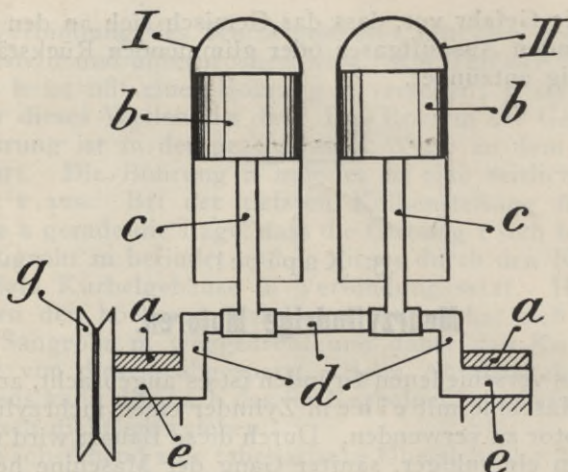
Schema eines Zweizylindermotors mit parallel stehenden Zylindern.
